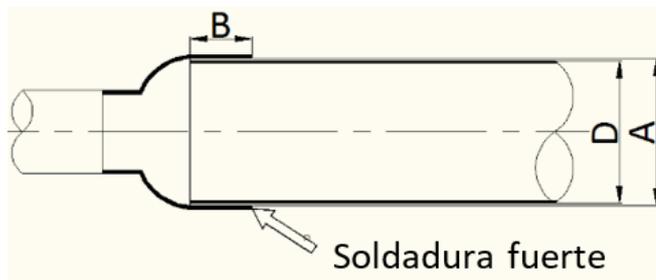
Orientación de las tuberías durante la soldadura
